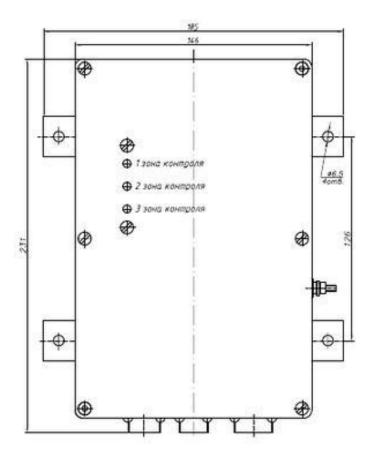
Габаритные и присоединительные размеры ВП МГДУ.
